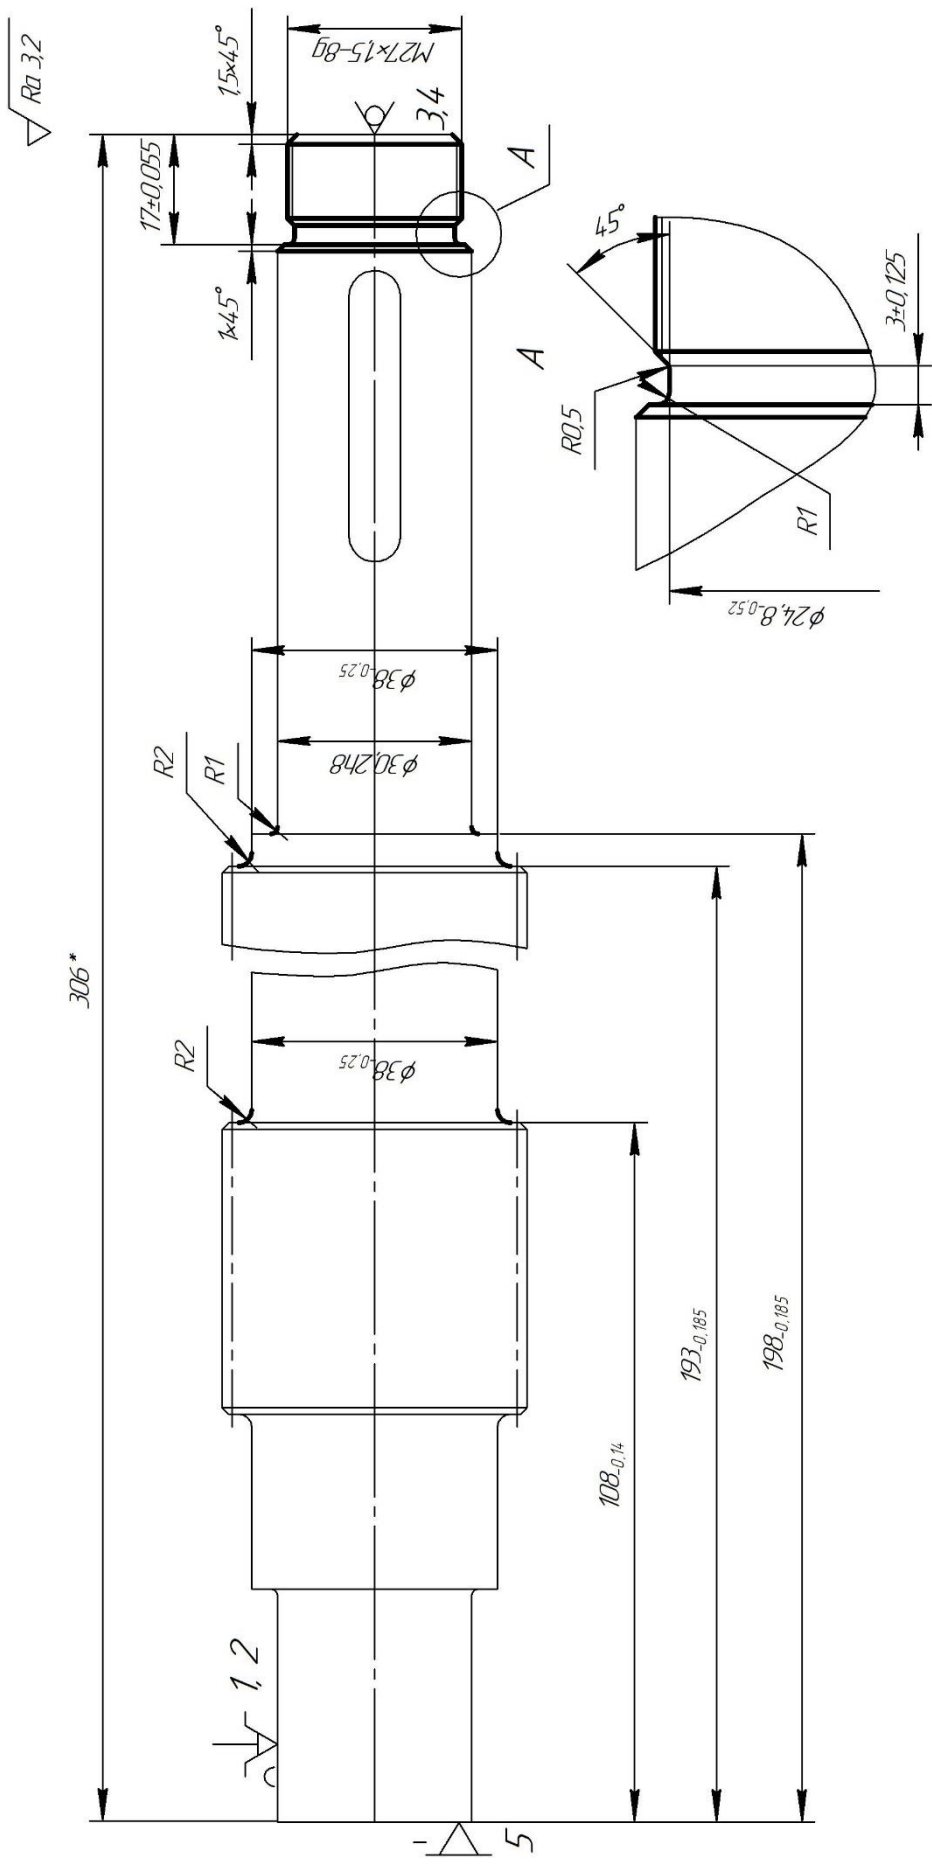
Альтернативна схема базування заготовки на операції 065 токарній з ЧПК, установ А
